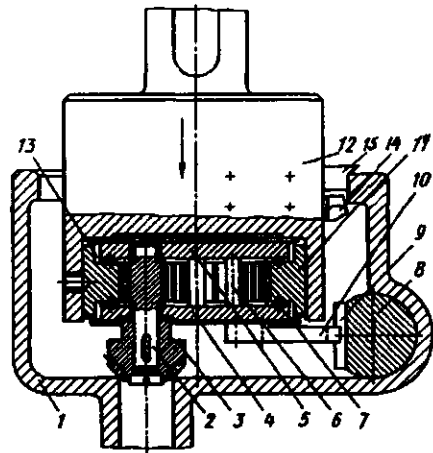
Инструментальная головка конструкции ЗИЛ для обработки отверстий, расположенных на расстоянии от оси вращения заготовки
